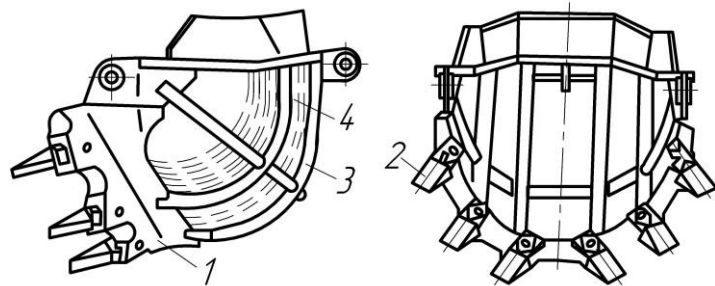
Схема каркасного ковша роздільного різання: 1 - кувалетний ковш; 2 - зуби; 3 - каркасний корпус; 4 - ланцюгове днище
